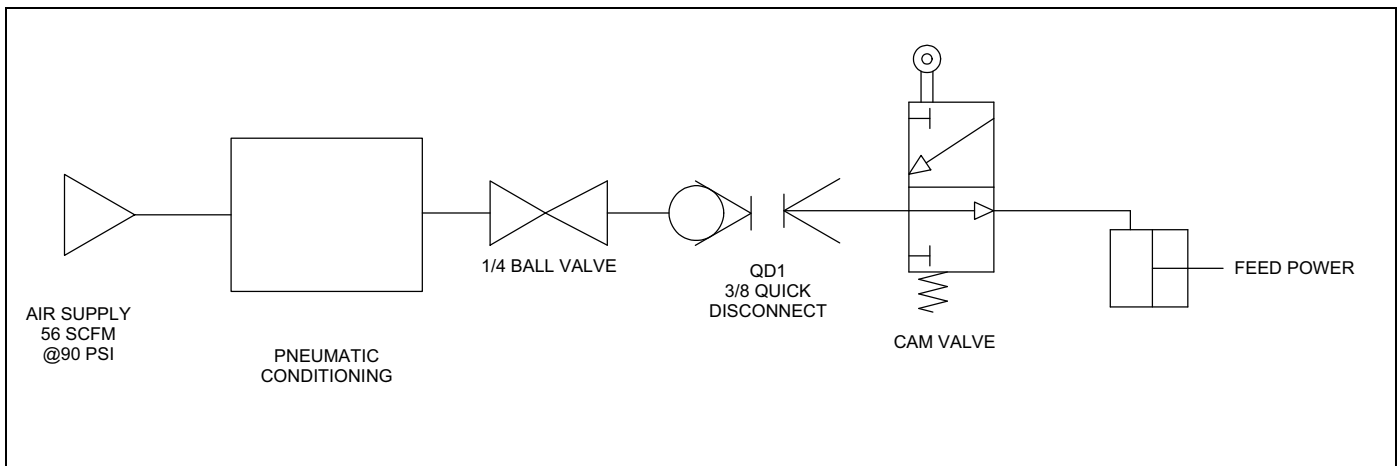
P/N 87941 SCHÉMA DE L'ENSEMBLE POUR AVANCE PNEUMATIQUE UNIQUEMENT (UTILISÉE AVEC DES MACHINES HYDRAULIQUES)
